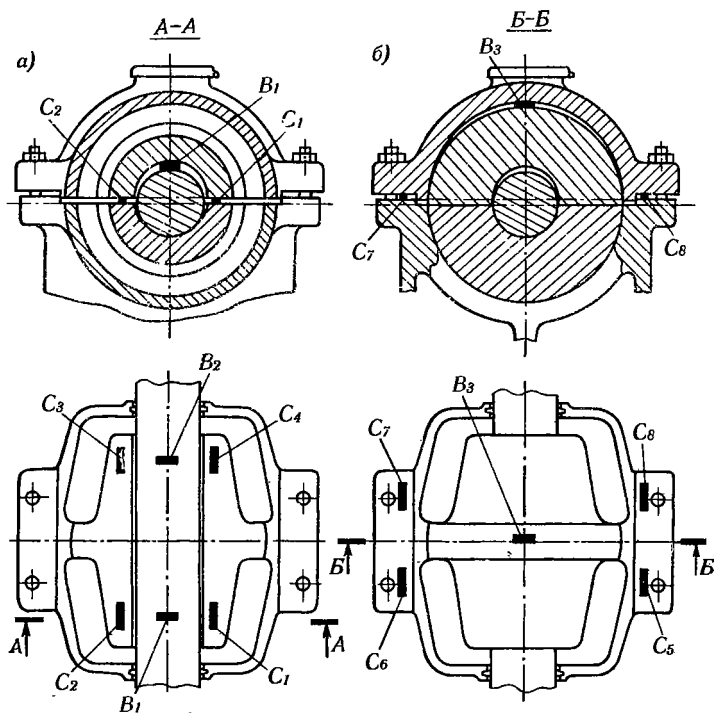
Измерение вертикального зазора: а — между шейкой вала и вкладышем, б — между крышкой подшипника и вкладышем
